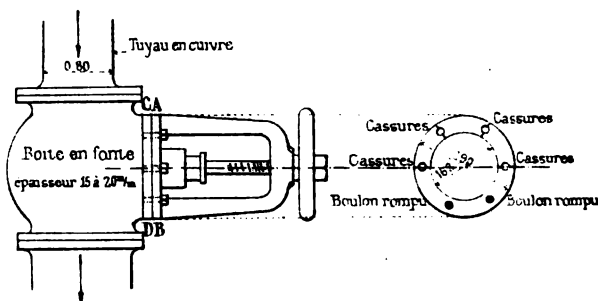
Détail de la valve (fig. 24) et indication des cassures de la bride CD.
